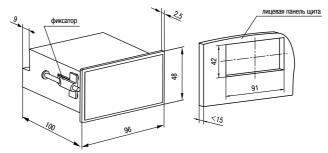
Габаритные размеры корпуса Щ2
